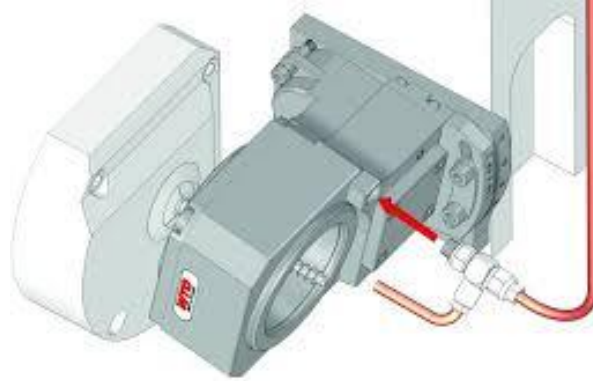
Привідний інструментальний блок верстата з ЧПК
